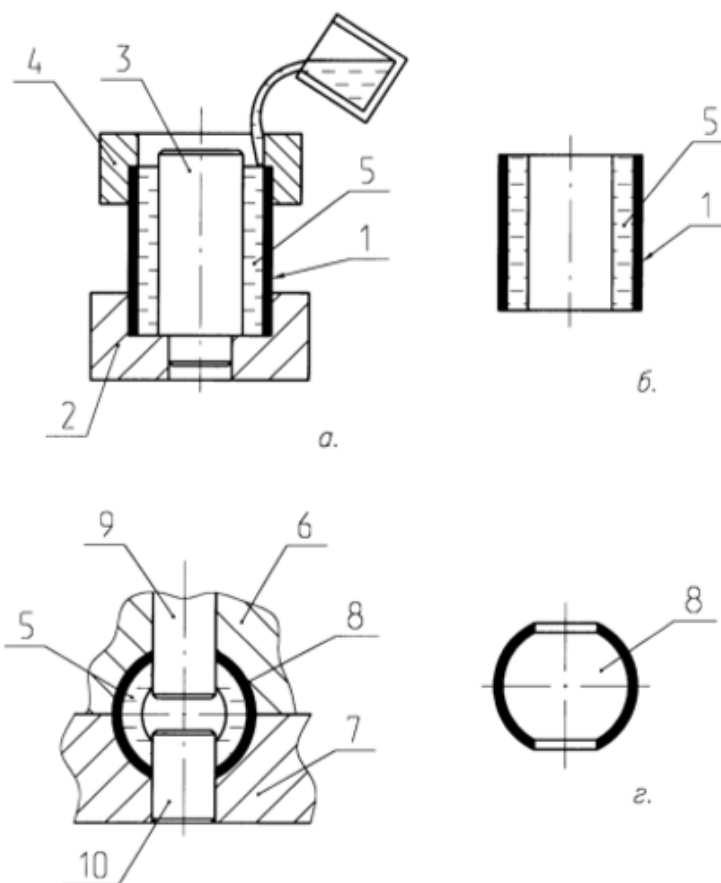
Схема обжима трубной заготовки с наполнителем: 1 – трубная заготовка, 2 – основание, 3 – оправка, 4 – втулка, 5 – наполнитель, 6 – верхняя полуматрица, 7 – нижняя полуматрица, 8 – готовое изделие, 9 и 10 – оправки обжимные
